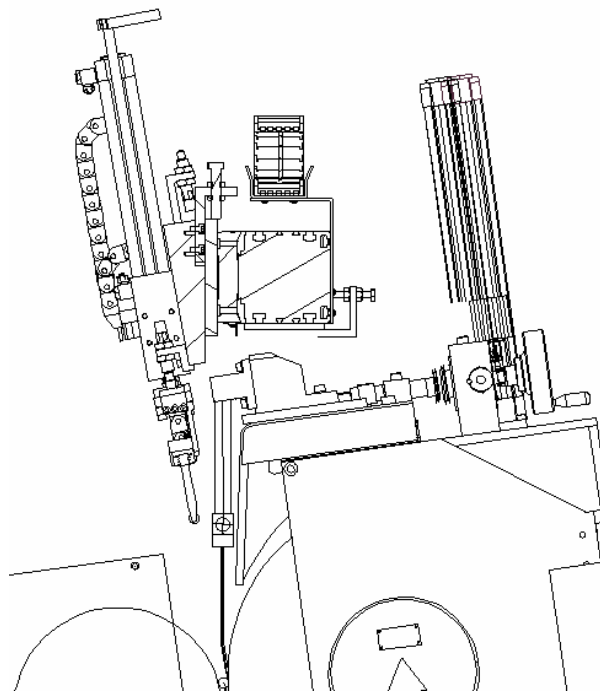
Svislý zdvih, 1-chapadlo, 2-spojovací člen, 3-vedení
